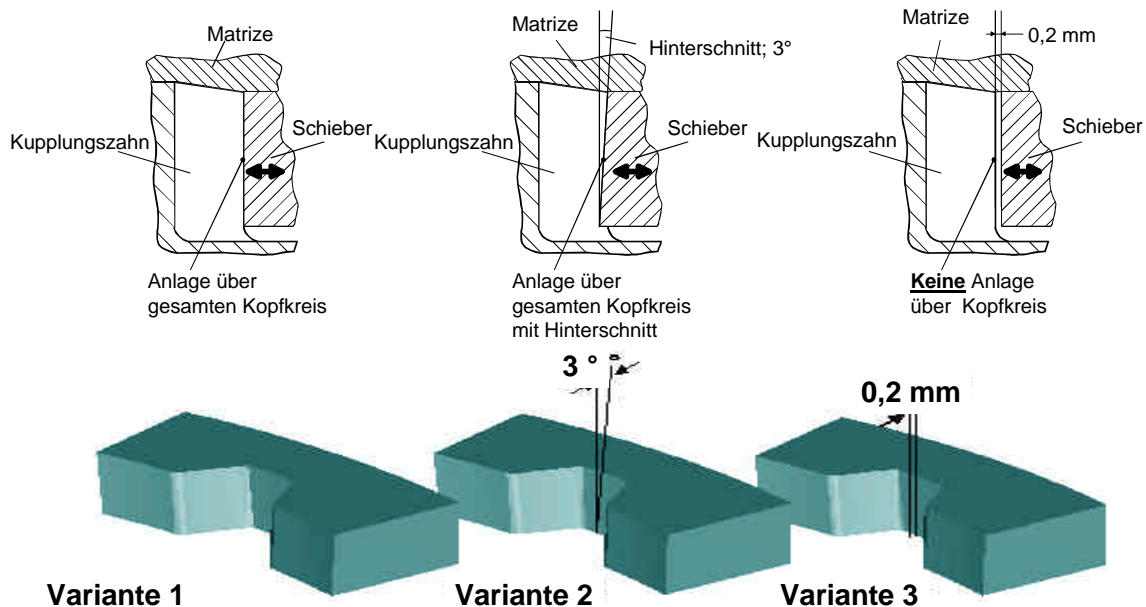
Werkzeugaufbau für die Simulation der Hinterschnitterzeugung
